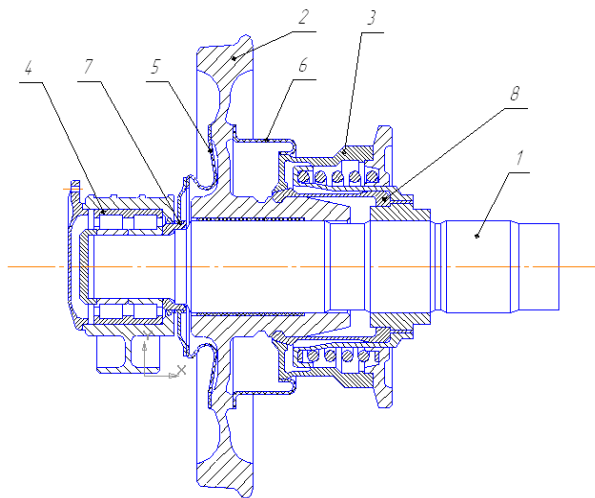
Базова модель системи SUW 2000: 1 – вісь; 2 – колесо; 3 – блокуюча втулка; 4 – підшипник; 5 – зовнішній кожух; 6 – внутрішній кожух; 7 – упорне кільце; 8 – цангова втулка
